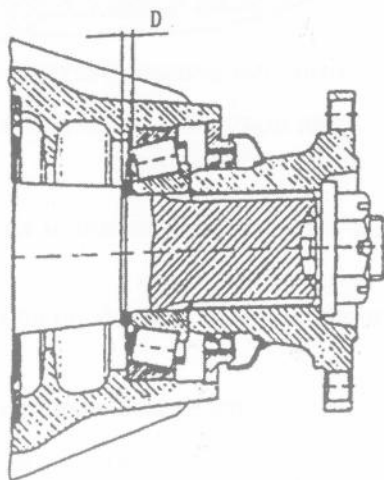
регулирующая шайба D предварительного натяжения подшипника ведущего конического колеса
